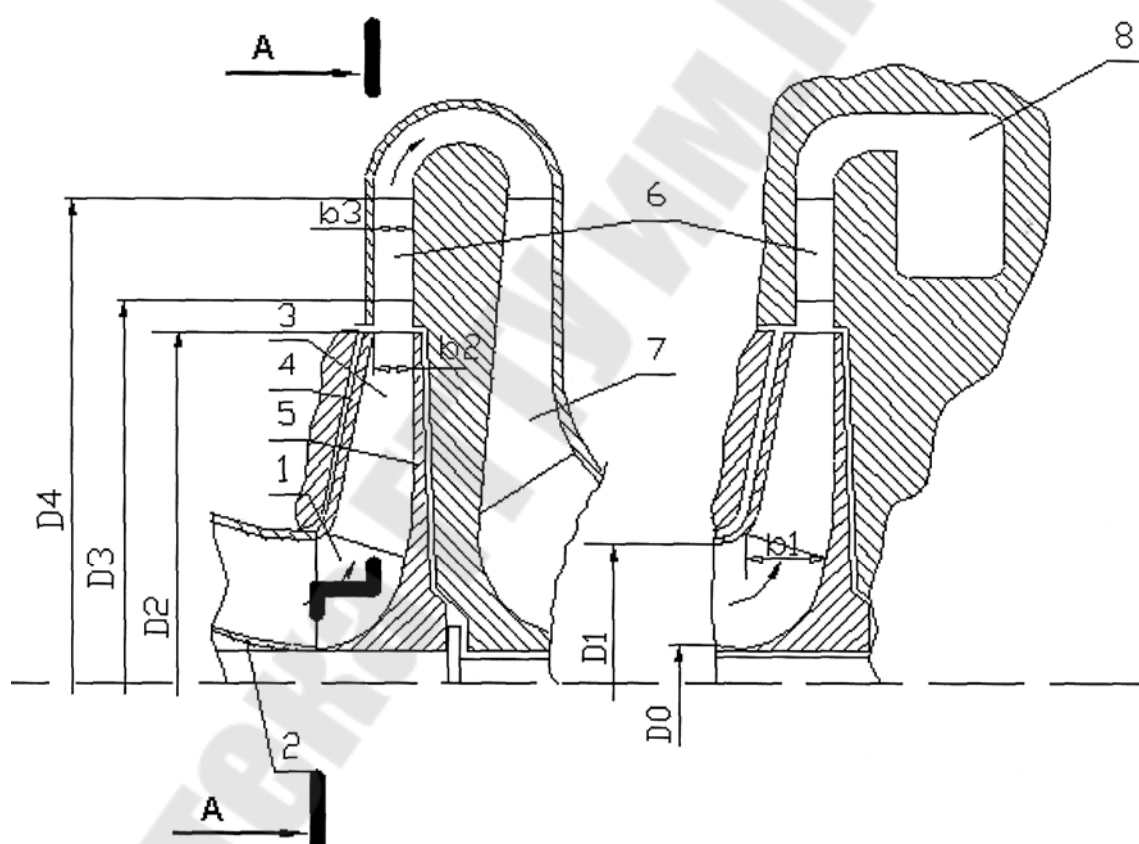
Продольный разрез ступени центробежного компрессора: а – начальная (промежуточная) ступень; б – конечная ступень; 1 – рабочее колесо; 2 – входное устройство; 3 – лопатка рабочего колеса; 4 – покрывной диск рабочего колеса; 5 – основной диск рабочего колеса; 6 – лопаточный диффузор; 7 – обратный направляющий аппарат; 8 – сборная камера (улитка).
